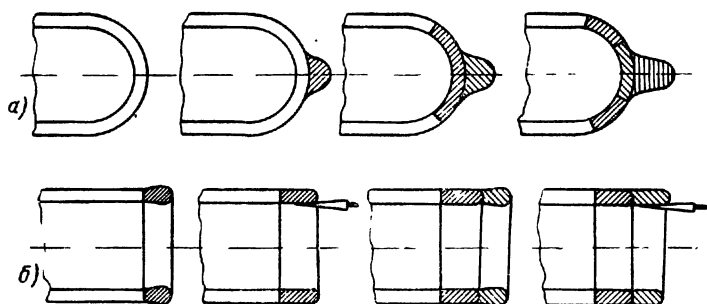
Изготовление переходного трубчатого спая кварцевого стекла:
